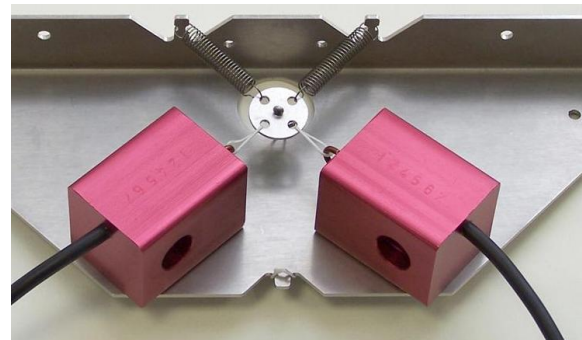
Fixação dos sensores de força no grupo de montagem de molas
